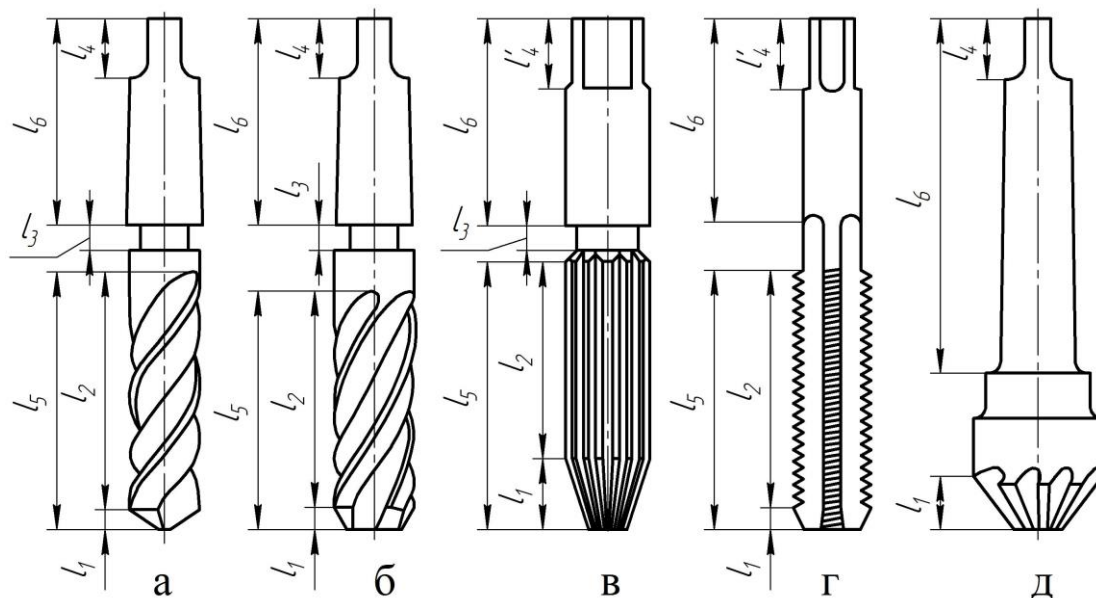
Різальні інструменти для обробки отворів:
